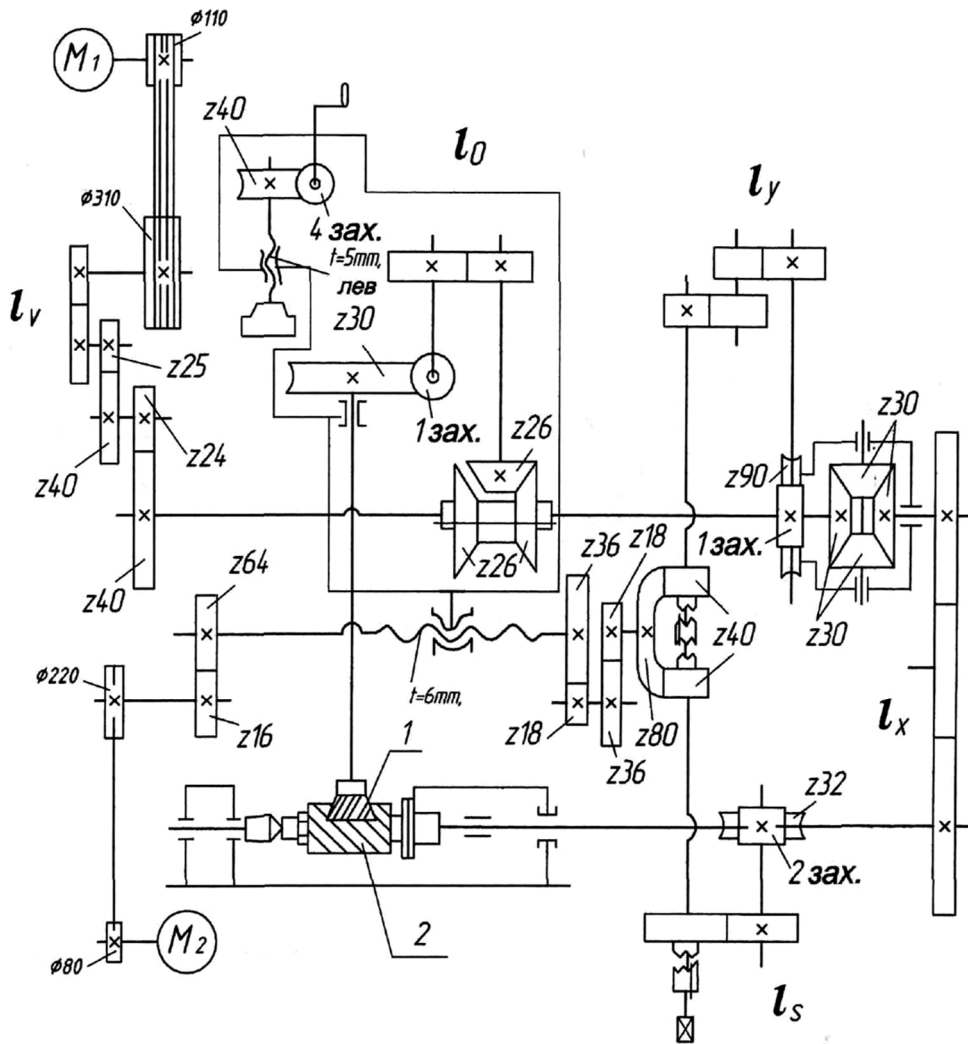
Кинематическая схема станка для нарезания цилиндрических червяков модели ЕЗ – 10А
